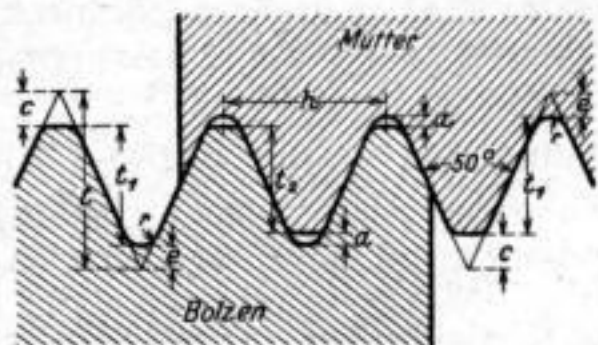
Profil des Schweizer Uhrmachergewindes für Schrauben unter 1 mm Durchmesser
